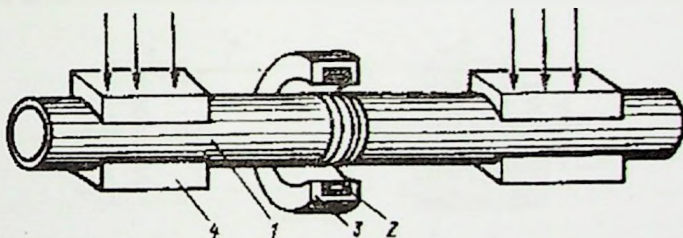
Схема стыковой высокочастотной сварки труб:
